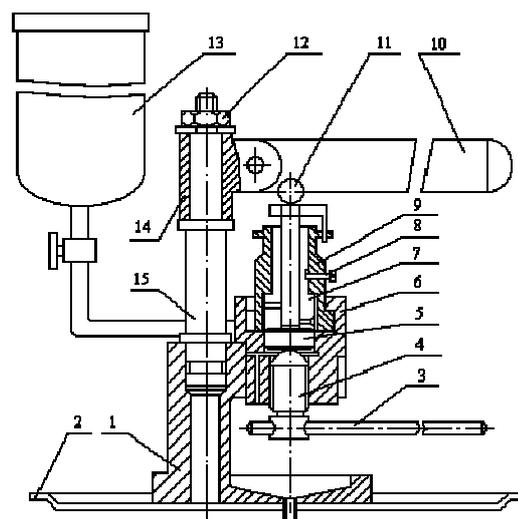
Устройство для проверки гидравлической плотности плунжерных пар: 1 – основание стойки; 2 – поддон; 3 – вороток; 4 – винт; 5 – подпятник; 6 – корпус установочного механизма плунжерной пары; 7 - втулка плунжера; 8 – стопорный винт втулки плунжера; 9 – установочная головка; 10 – рычаг; 11 – ролик; 12 – гайка; 13 – емкость для топлива; 14 – втулка; 15 – стойка.
